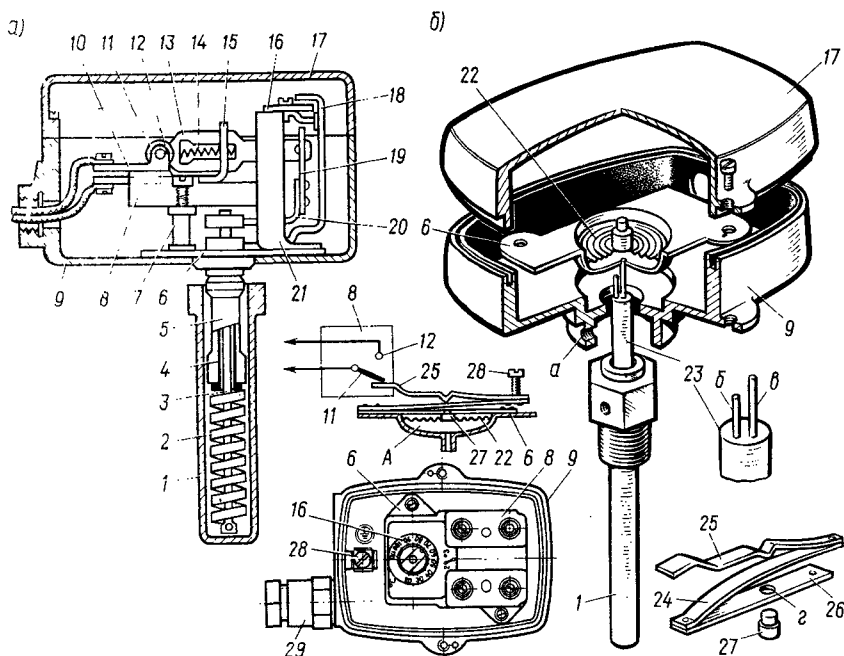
Термореле типа ТSC17А2 (а) и "Саутер ТСЦВА108Л10" (б): 1 — защитный кожух; 2 — биметаллическая спираль; 3 — стержень; 4 — трубка; 5 — направляющая втулка; 6 — стальная пластина; 7 — стойка; 8 — панель; 9 — корпус; 10, 15 — латунные пластины; 11, 12 — подвижный и неподвижный контакты; 13 — рычаг; 14 — пружина; 16 — шкала; 17 — крышка; 18 — поворотный рычаг; 19 — рамка; 20 — поводок; 21 — фигурная стойка; 22 — мембрана; 23 — термобаллон; 24, 26 — пластинки; 25 — качалка; 27 — шпенец; 28 — регулировочный винт; 29 — штуцер; А — камера; а, з — отверстия; б, в — трубочки
